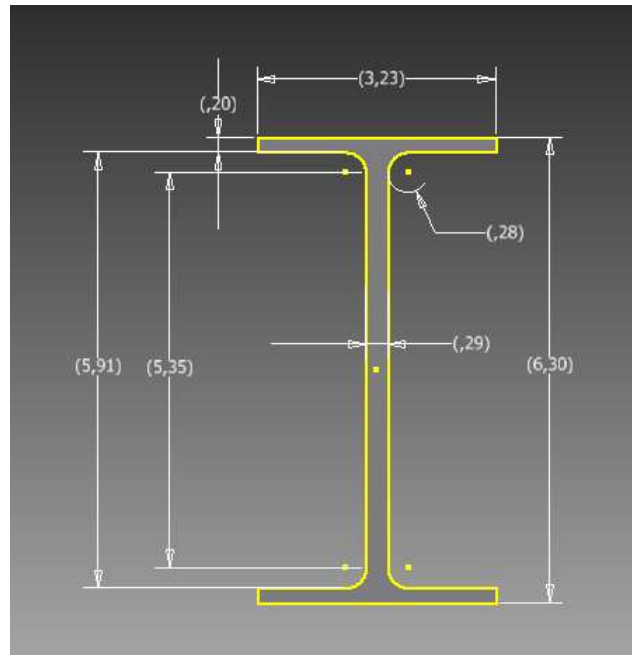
DIMENSIONES DE LA VIGA PRINCIPAL IPE 160
